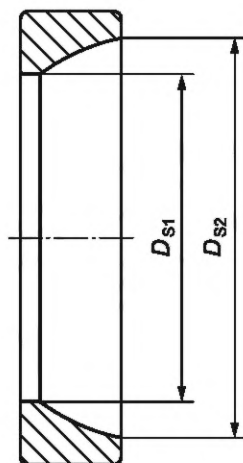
Наружное кольцо радиально-упорного шарнирного подшипника
